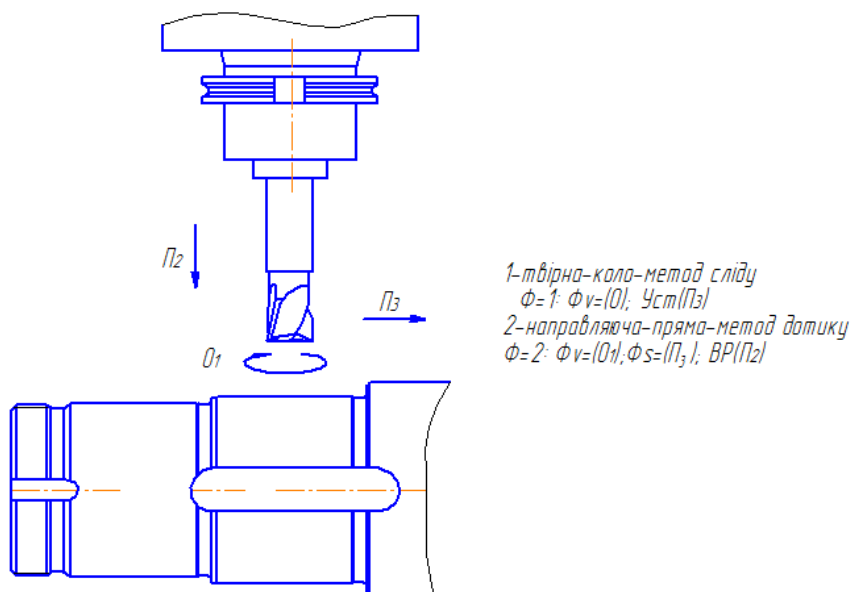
Комплекс формоутворюючих рухів при обробці шпонкового пазу
